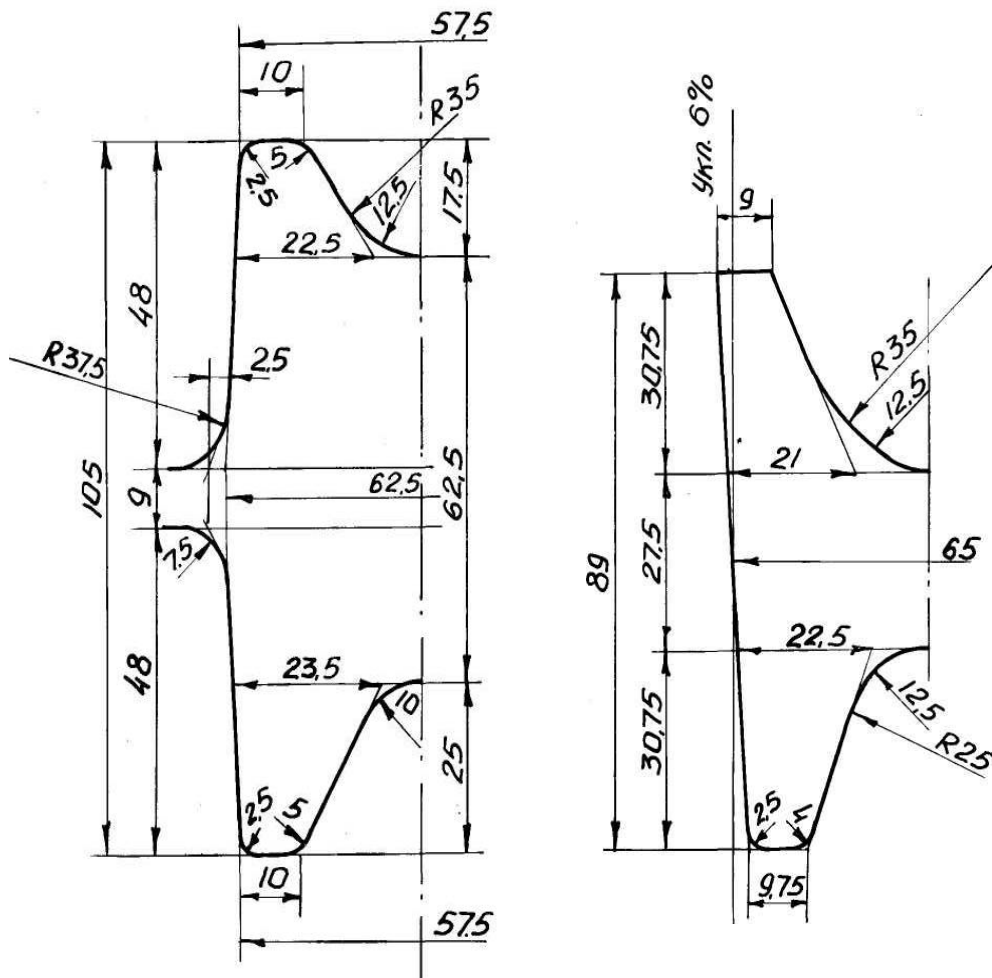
Розрахункова схема розрізного та наступного для нього калібрів
